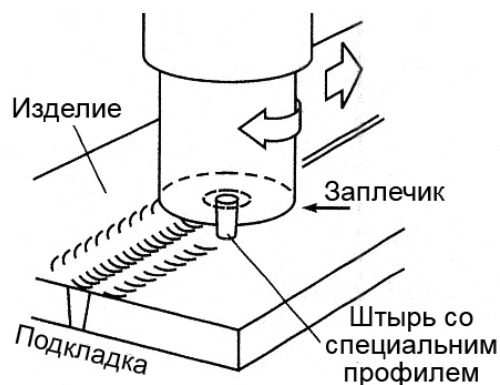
Схема процесса сварки трением с перемешиванием
